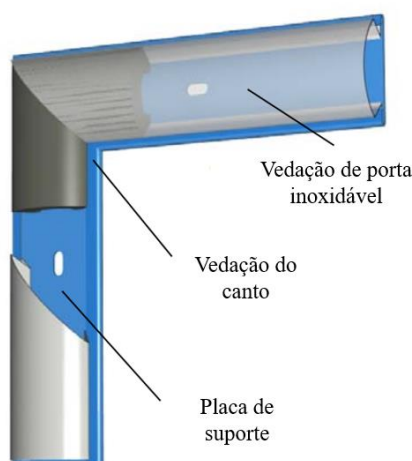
Sistema Quick-Change Dryer Door Seal da Westmill Industries (Documentação técnica)
